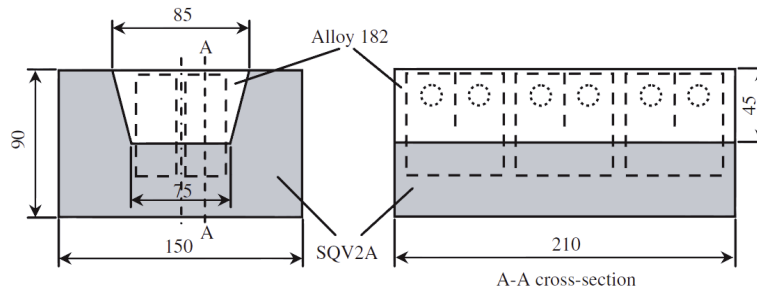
Prélèvement des éprouvettes dans la soudure [OGA 12]
